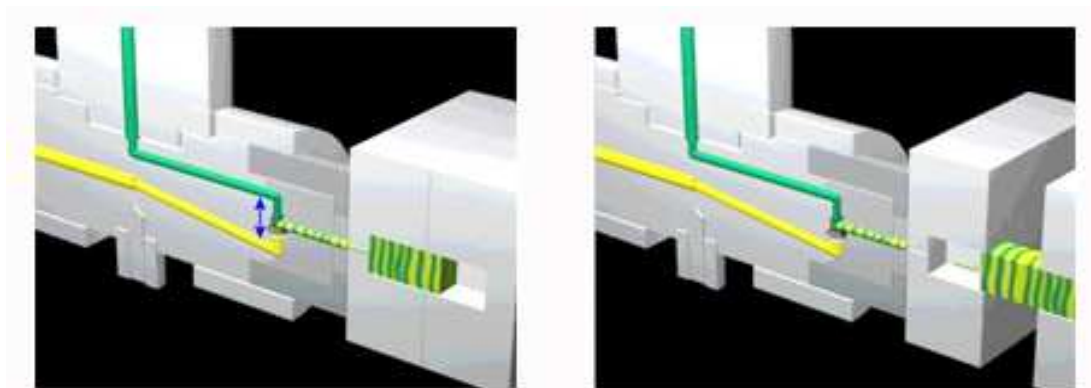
Princip použití posuvné části formy – šoupátka [3]
